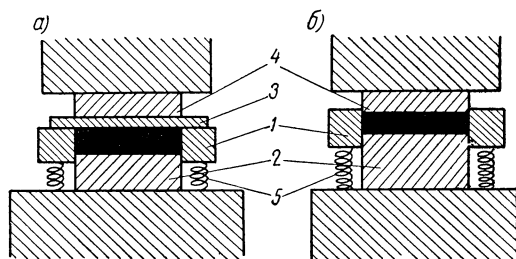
Схема стационарной прессформы для последовательного двухстороннего прессования крупногабаритных заготовок: а — первое прессование, подача давления снизу; б — второе прессование, подача давления сверху.
